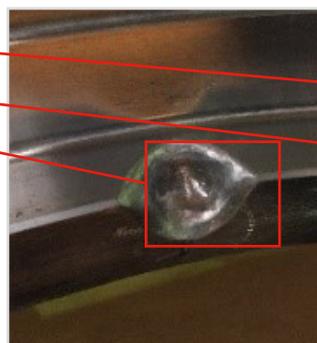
Beseitigung des Fehlers und Schweißen
